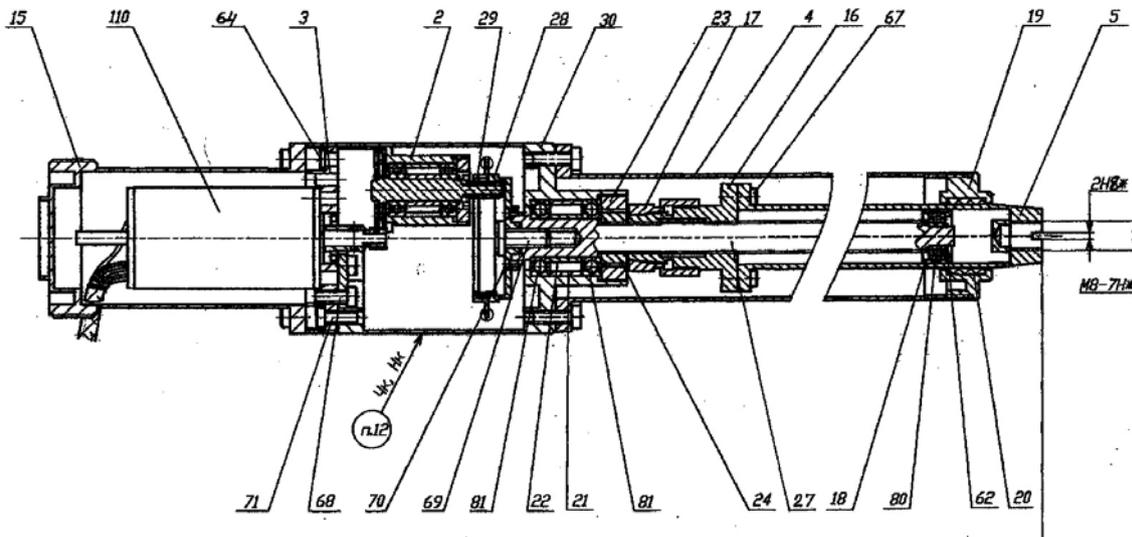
Общий вид линейного привода для макета шестистепенного привода типа «гексапод»
